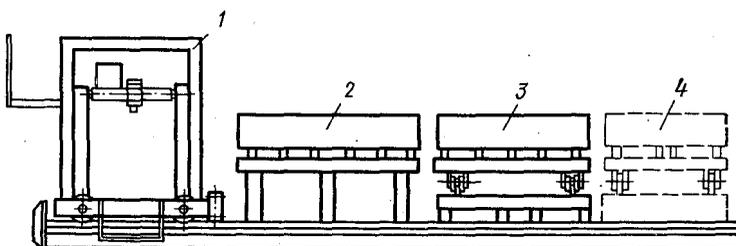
Схема стапеля для сборки и сварки секций крыши
